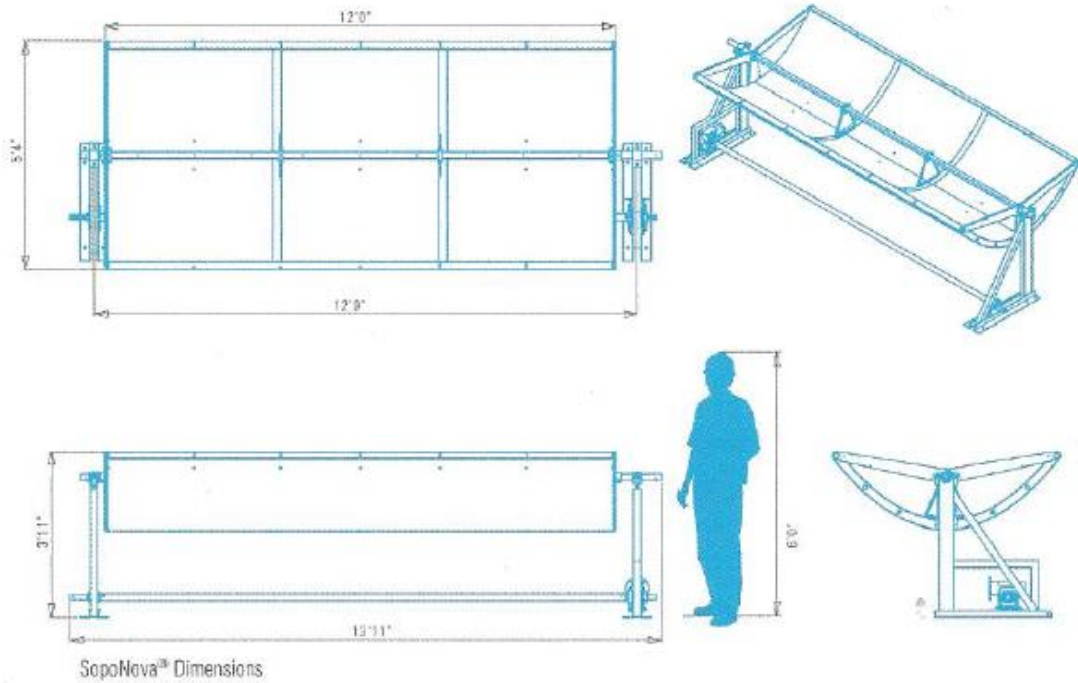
Dimensiones de colector solar SopoNova® 4.1. Fuente: Folleto técnico SOPOGY.
